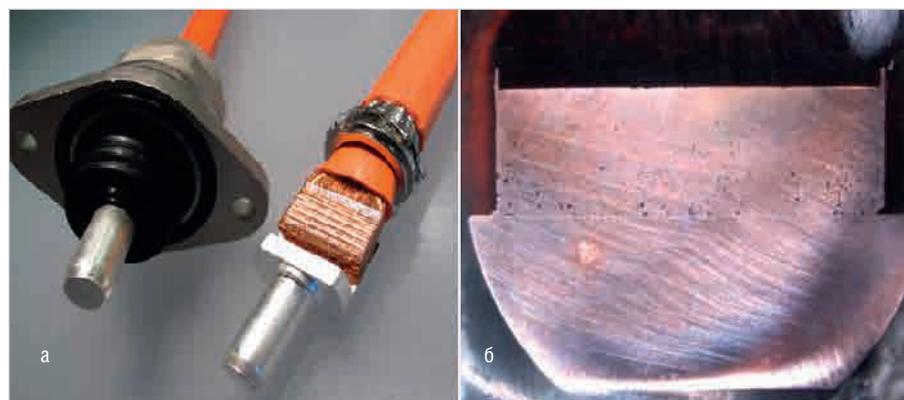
Ультразвуковая сварка провода сечением 95 мм² с терминалом Impregium: а) внешний вид сплава терминала и провода; б) разрез зоны ультразвуковой сварки
